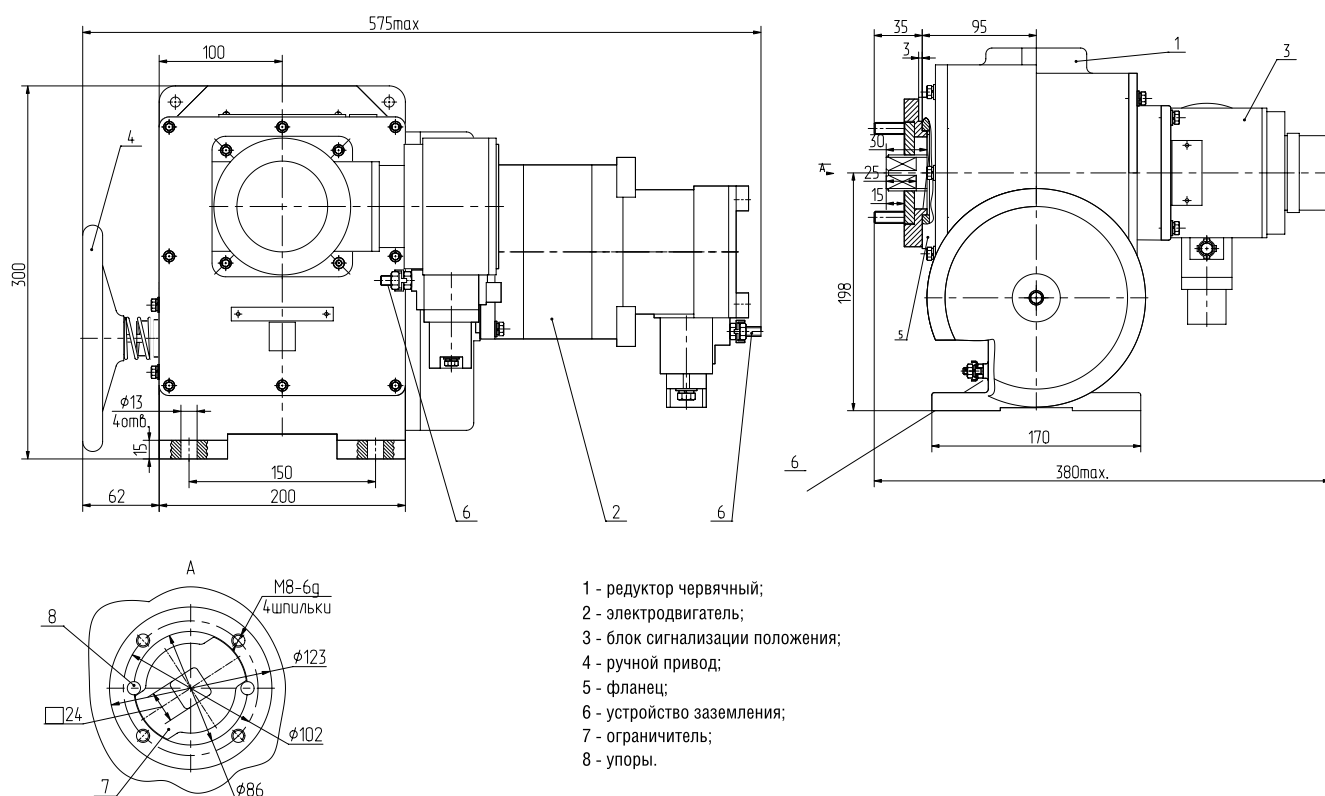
Габаритные и присоединительные размеры М30Ф-250-ИБТ4
